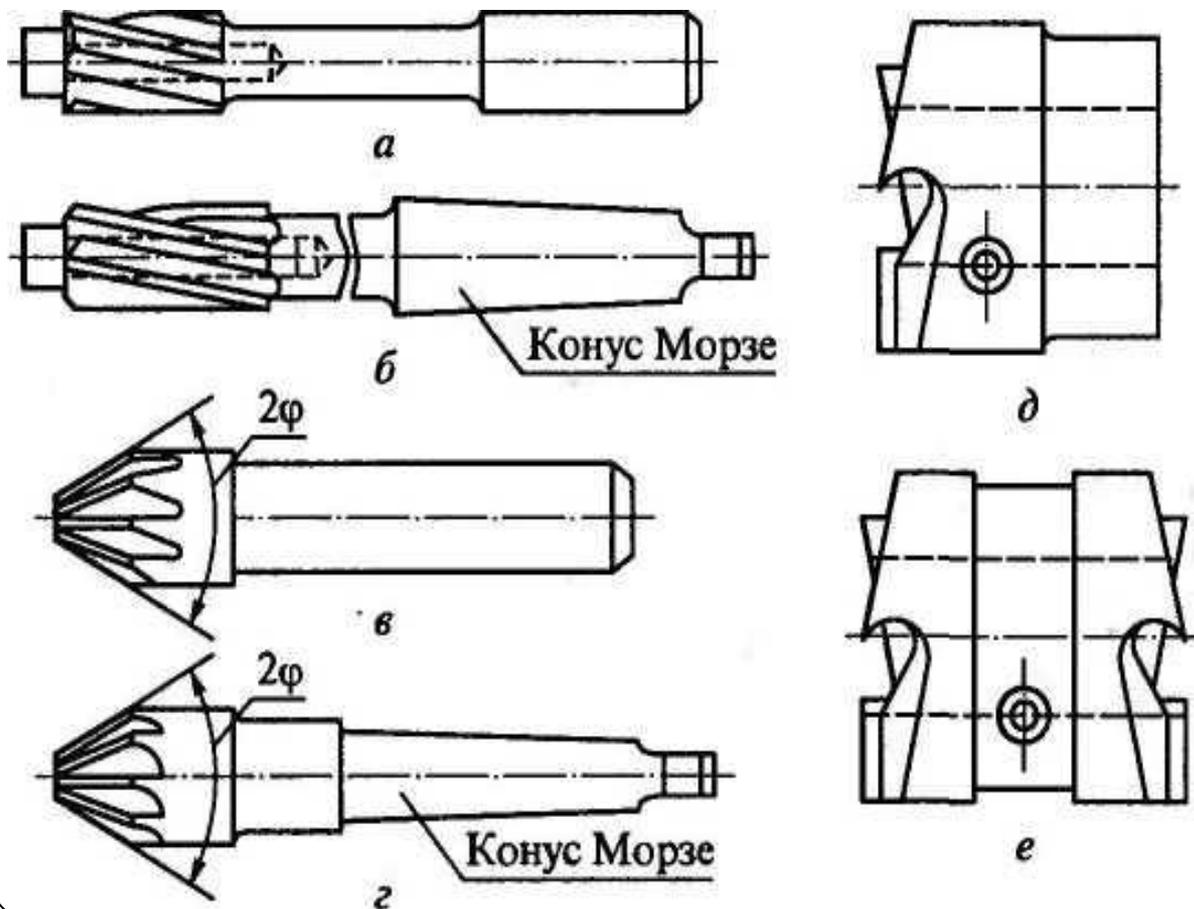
Зенковки и цековки: а, б - цилиндрические; в, г - конические; д, е - цековки насадные; 2φ - угол при вершине
